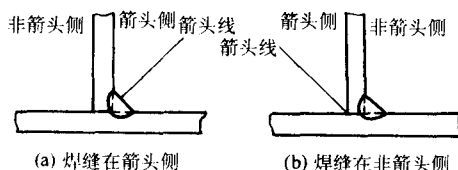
焊接接头的箭头侧和非箭头侧
